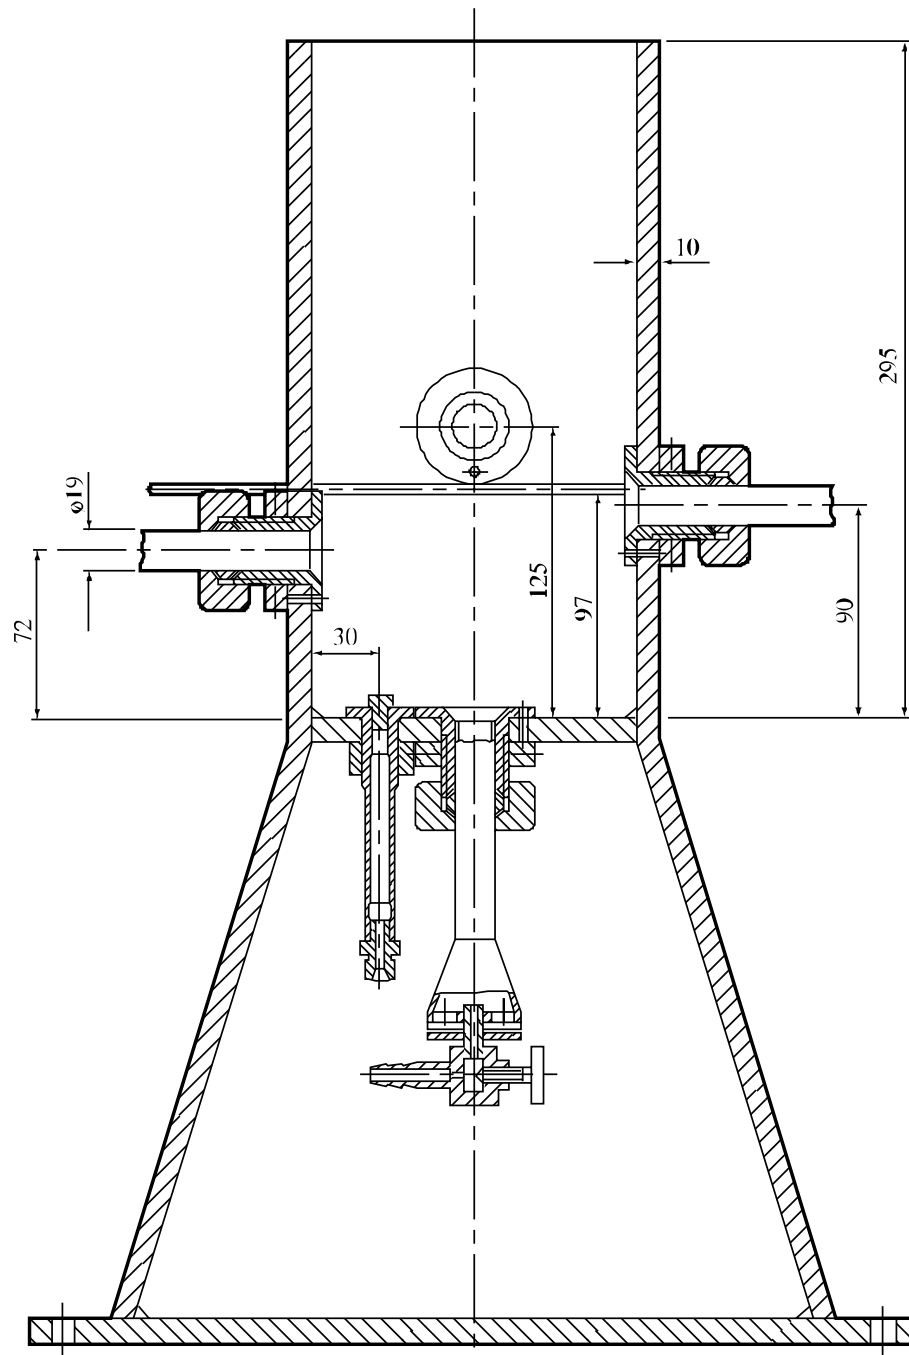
ЗАЩИТНО-НАГРЕВАТЕЛЬНОЕ УСТРОЙСТВО
